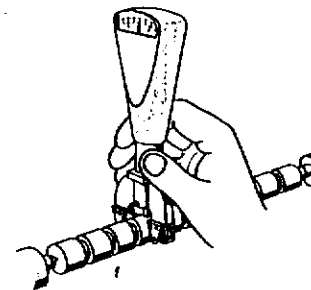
Ajuste del calibre de caballete mediante varilla patrón.
